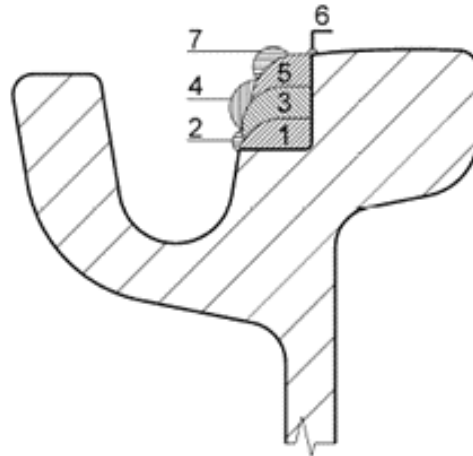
Auftragschweißen an der Fahrflanke
